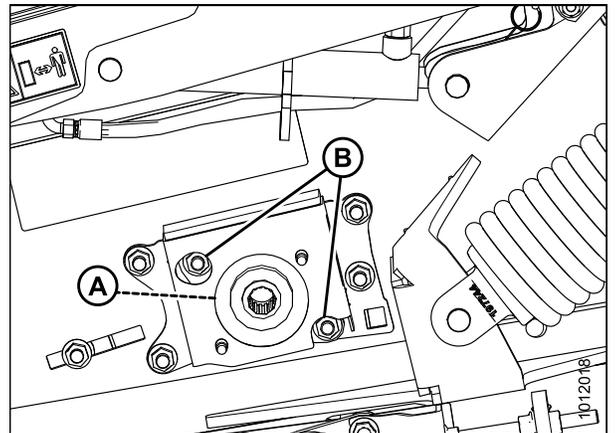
Rodillo de mando de la cama frontal del lado izquierdo
